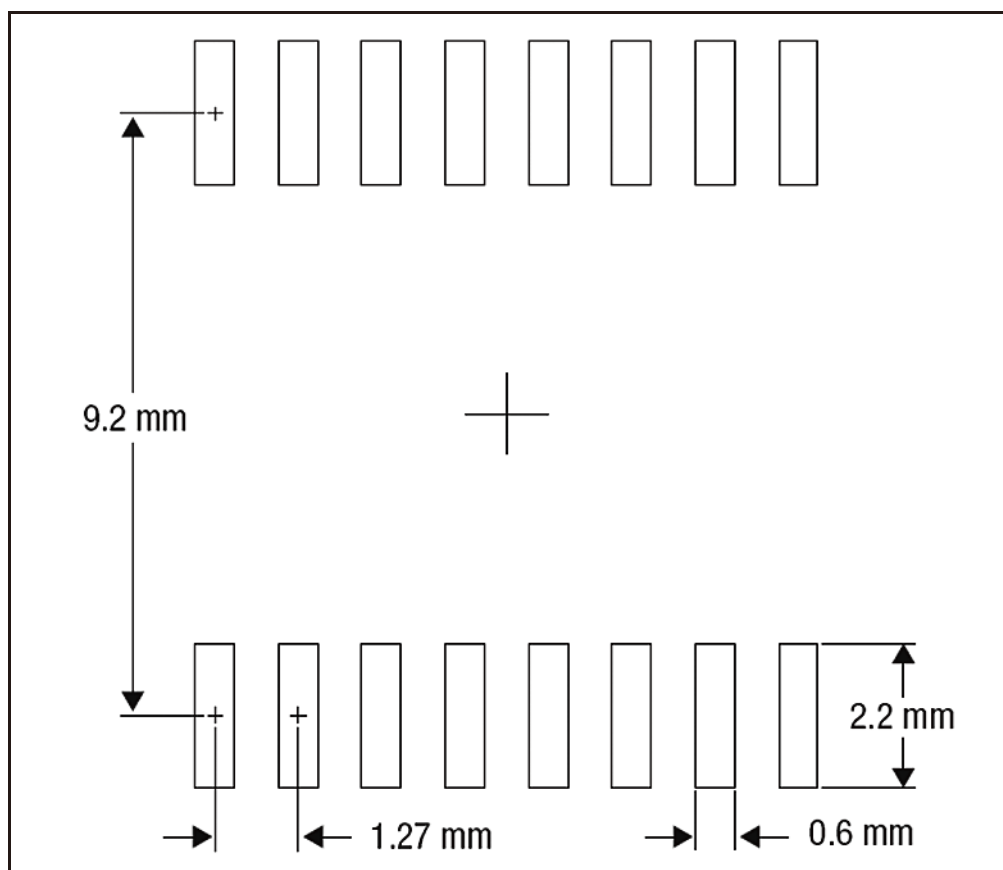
推荐的 PCB 焊盘布局 (SOIC 14 宽包)
